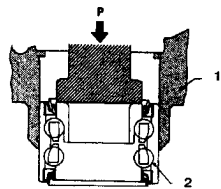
Снятие подшипника со ступицы (См. Раздел 6)
